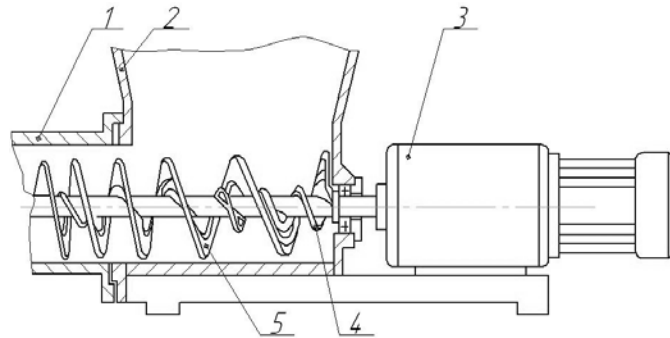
Транспортуючий механізм вовчка: 1 - корпус; 2 - бункер; 3 - привід; 4 - внутрішня навивка шнека; 5 - стрічкова спіраль
